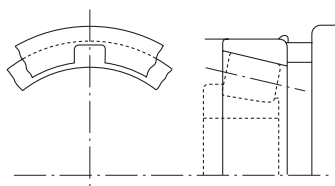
Канавки в корпусе конического роликоподшипника для демонтажа
